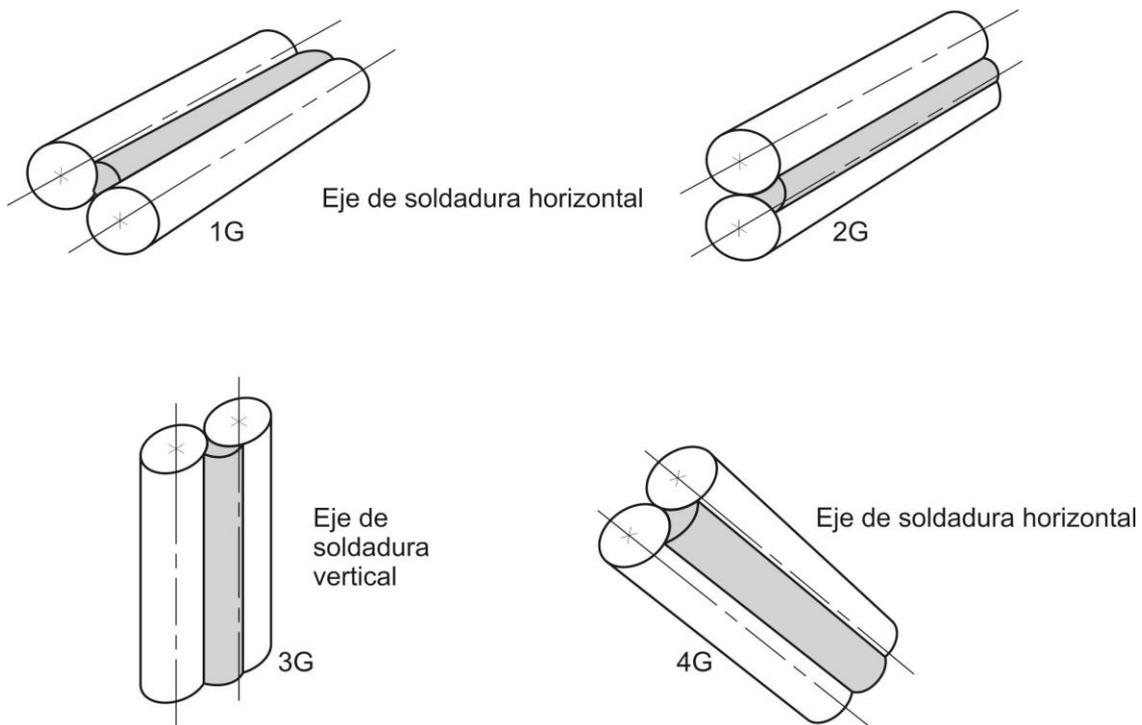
Posiciones de soldadura para la calificación de probetas en uniones a tope indirectas y de empalmes de yuxtaposición simples y dobles con juntas acampanadas o de filete.
